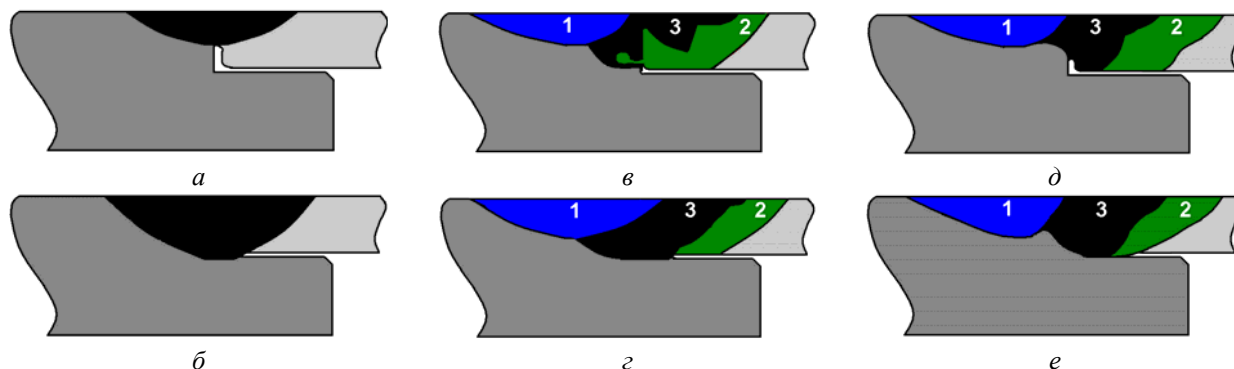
Схема формирования сварных соединений: а, б - Э110-Э110 и ВТ1-ВТ1; в, г - Э110-ГФЭ-1; д, е - ВТ1-ГФЭ-1
